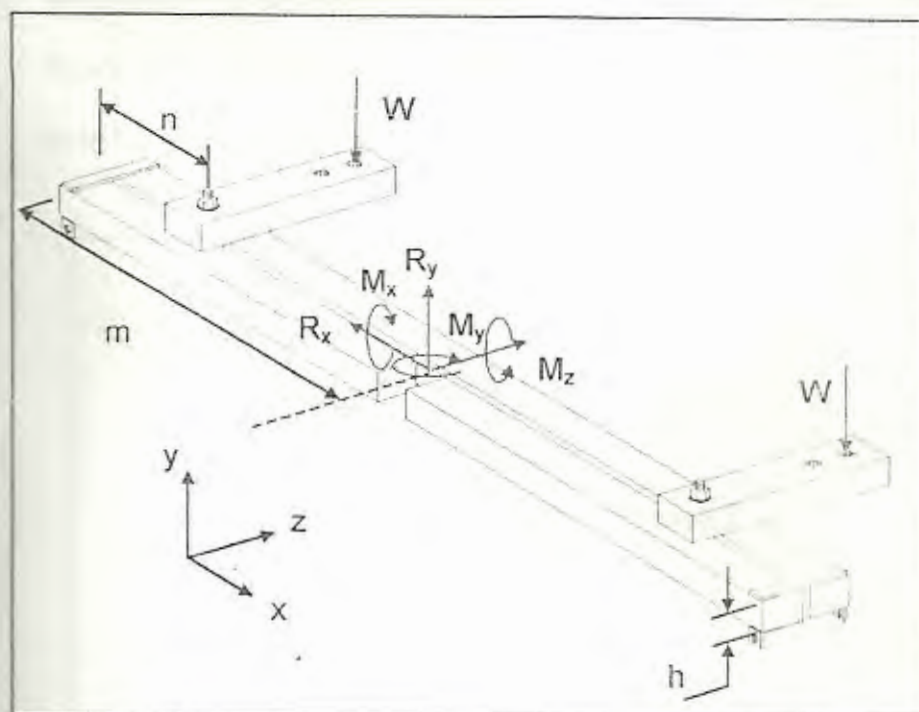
DIAGRAMA DE VIGAS LONGITUDINALES
